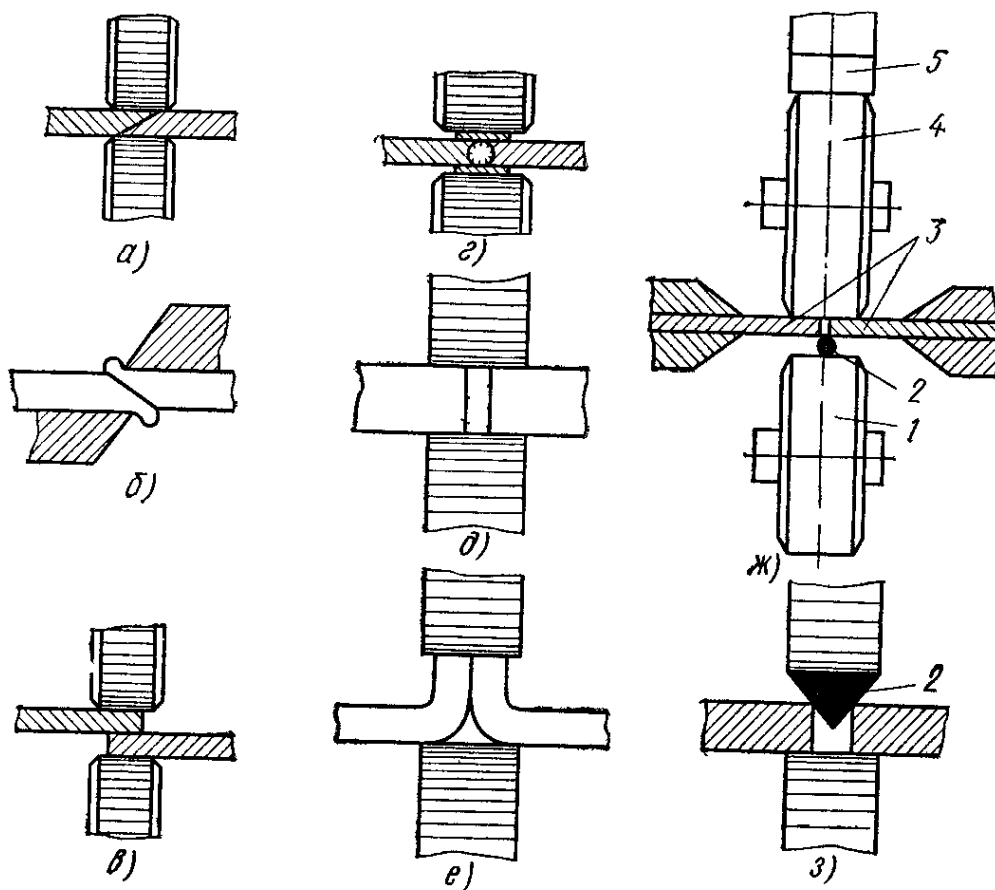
Разновидности шовно-стыковой сварки:
